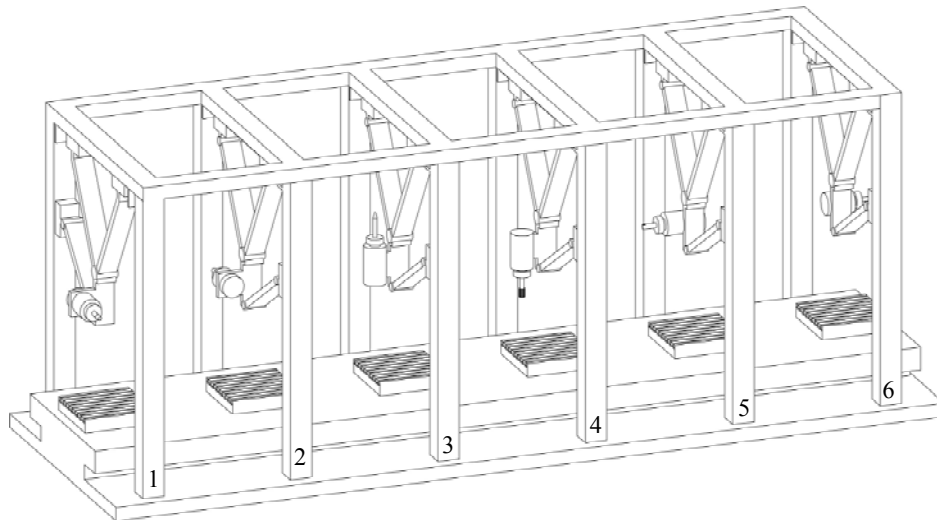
Об'єднана компоновка свердильно-фрезерного верстату з різною початковою орієнтацією шпинделя
